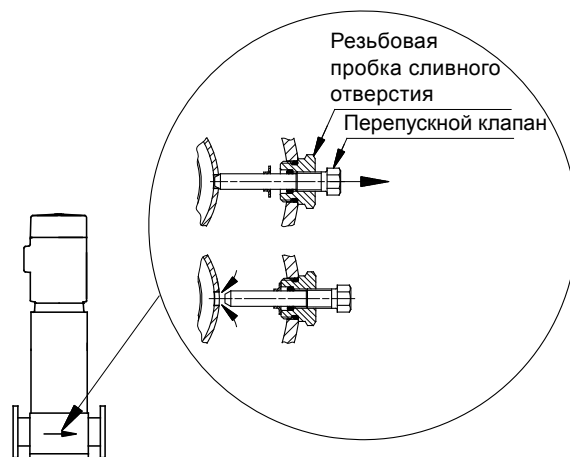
Местоположение резьбовой пробки сливного отверстия с перепускным клапаном
